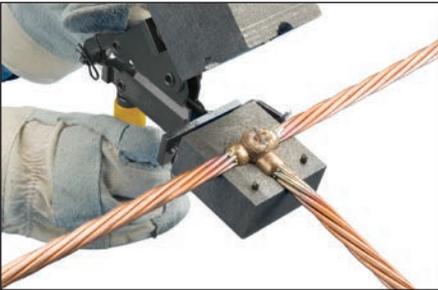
Abra el molde y retire la conexión. Tenga cuidado para evitar dañar el molde. Evite el contacto con materiales calientes. Consulte la sección “Normas de calidad nVent ERICO Cadweld” para ver si se ha realizado una conexión de calidad.
